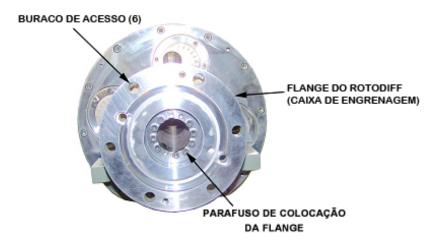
Conexão da Caixa de Engrenagem ao flange
